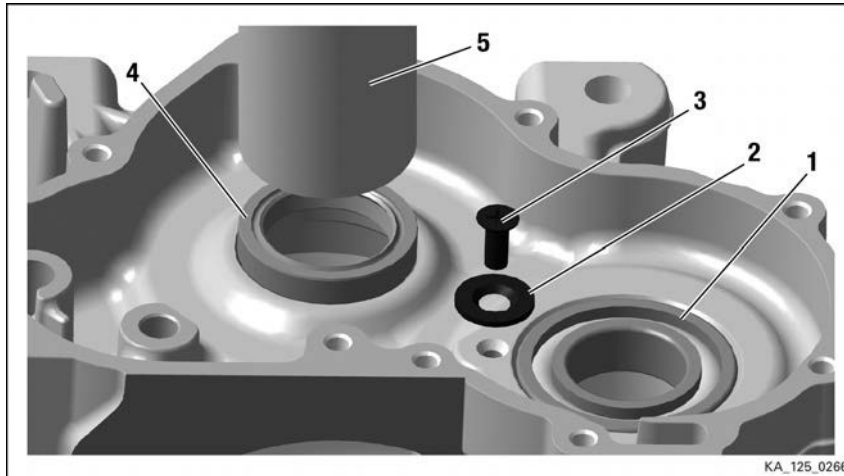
Ball bearing, oil seal 滾珠軸承、油封
